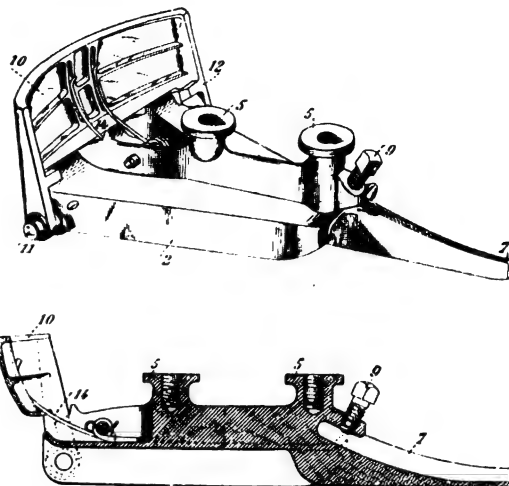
et 30. — Contact pour ponts tournants de Potter. Vue d'ensemble et coupe.
